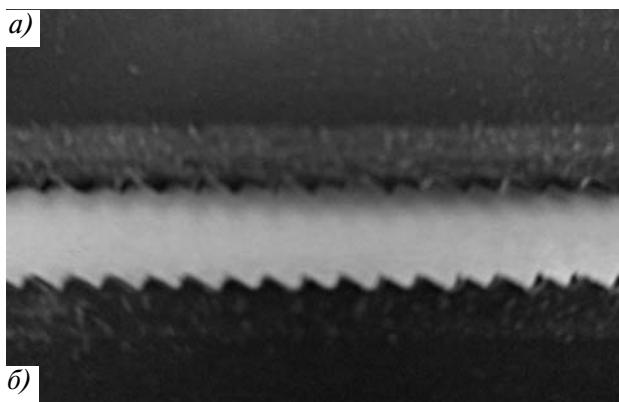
Полотно для ножовки из стали У10А после испытания:
